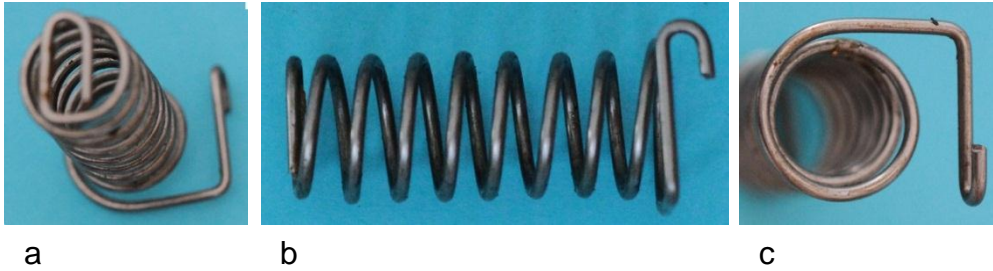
Druckfeder: a) Seite Feder zur Befestigung am Drehbolzen, b) Entspannte Druckfeder, c) Federende zum Einhängen am Bedienungshebel
